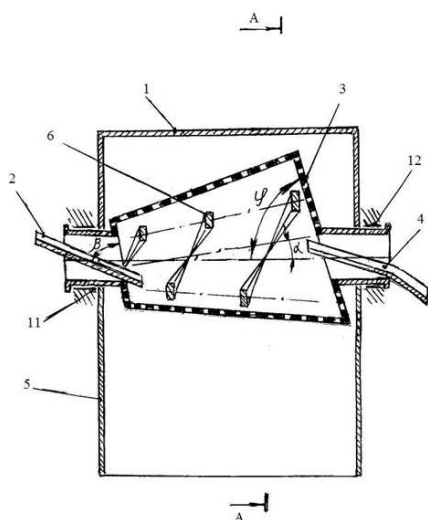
Машина для обезвоживания навоза, вид спереди
